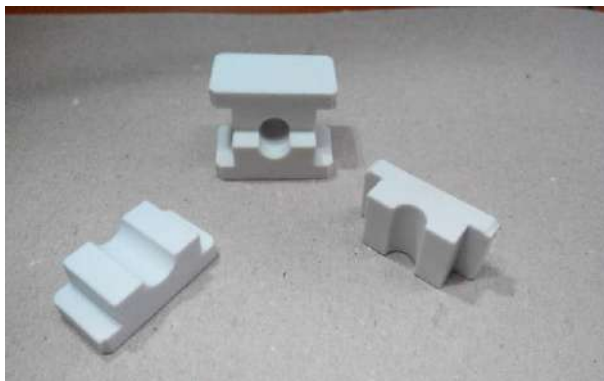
Керамические изоляторы для автоматической сварки биметаллических трубчатых элементов
